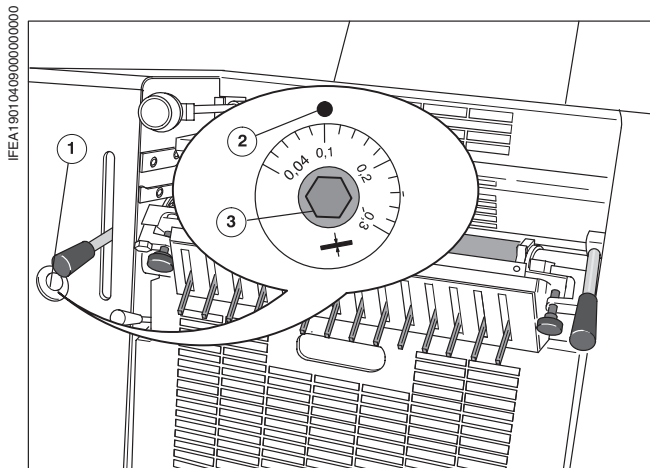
Давление: офсетный цилиндр - печатный цилиндр.
